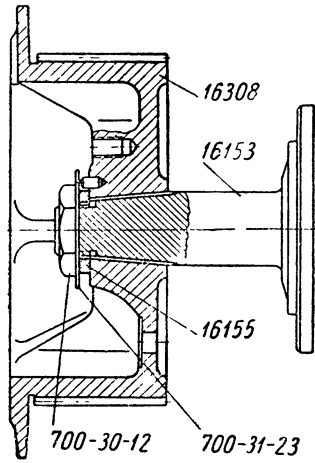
Ведущий вал главной передачи с конической шестерней.
